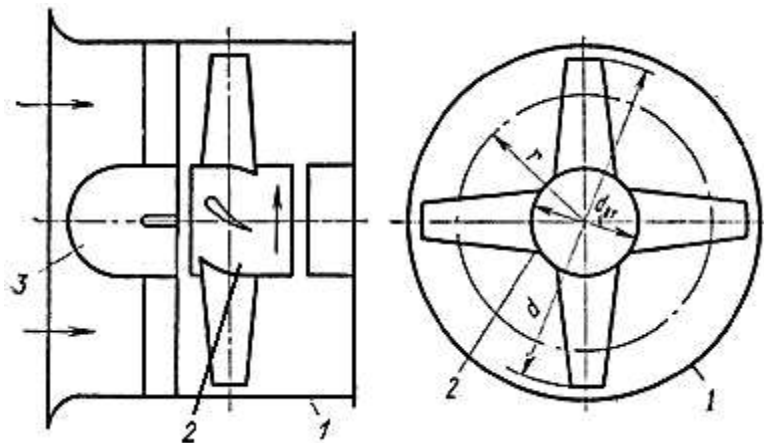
Схема осьового вентилятора: 1 - корпус; 2 - робоче колесо; 3 - обтічник
